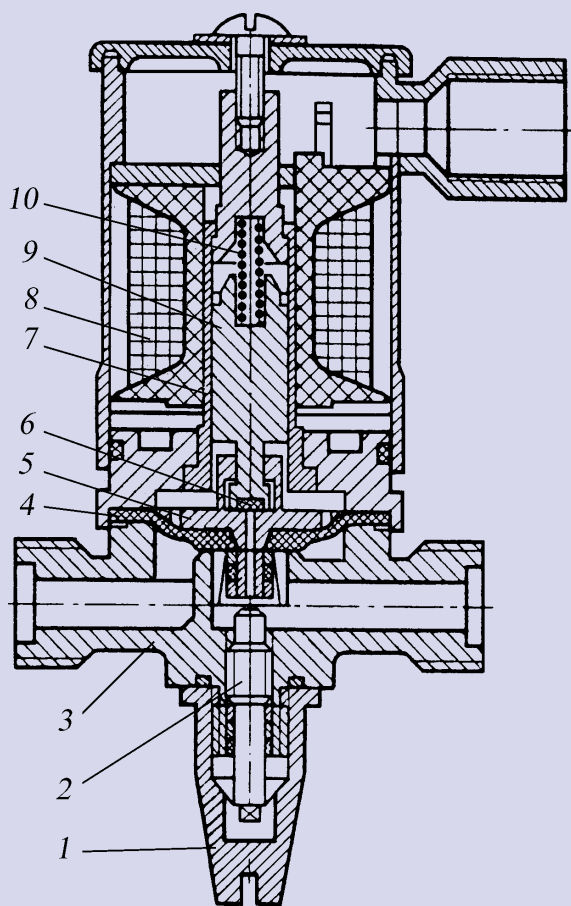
Магнитный вентиль ПЗ 26237-015: 1 — колпачок; 2 — винт; 3 — корпус; 4 — мембрана; 5 — основной клапан; 6 — вспомогательный клапан; 7 — направляющая трубка; 8 — электромагнит; 9 — сердечник; 10 — пружина
